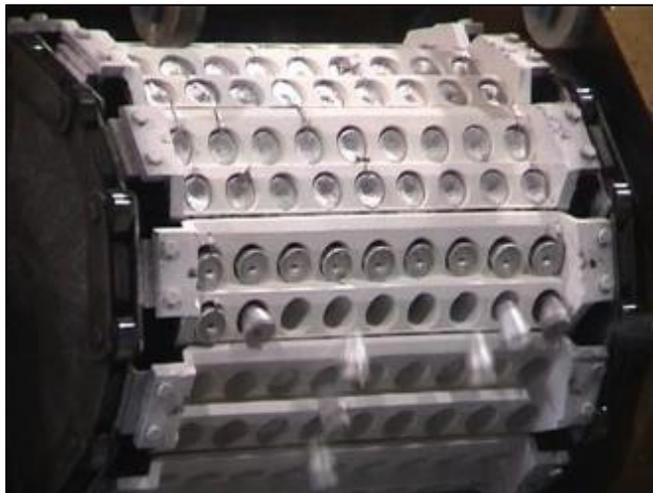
Correa con moldes de conos (Cone Casting Machine).
